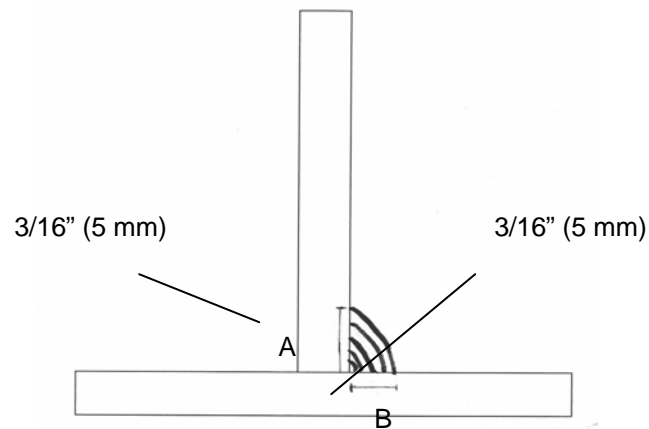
Cordón de soldadura bien aplicado A = B
